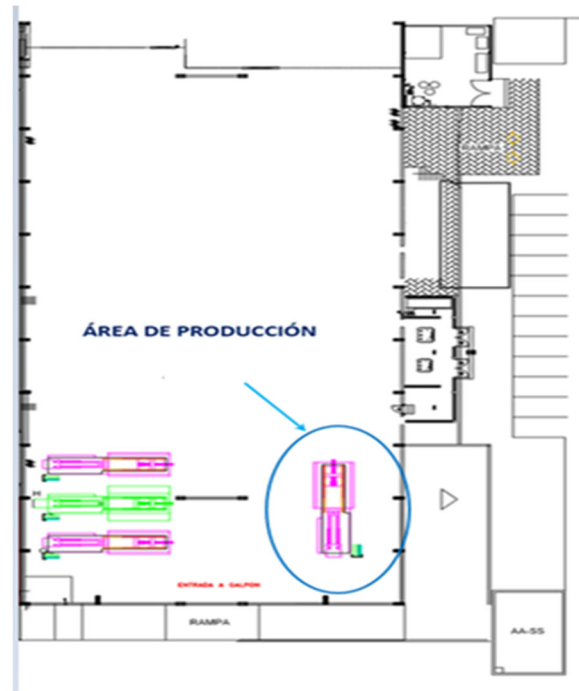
Esquema donde irá ubicado el equipo en la Planta
